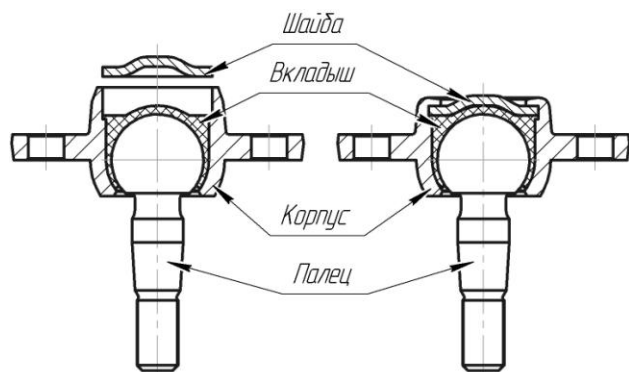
Шаровой шарнир с соединением КВ до и после сборки
